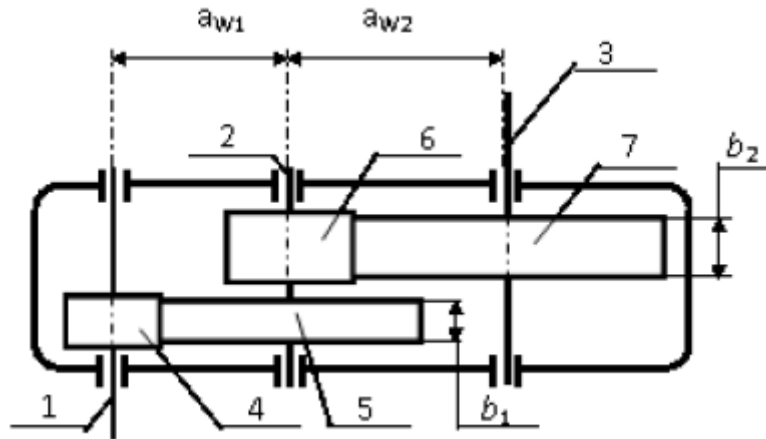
Кинематическая схема двухступенчатого цилиндрического редуктора:
